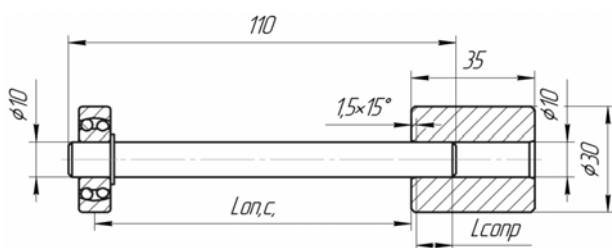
Эскиз соединения с натягом с напрессованным на вал подшипником
